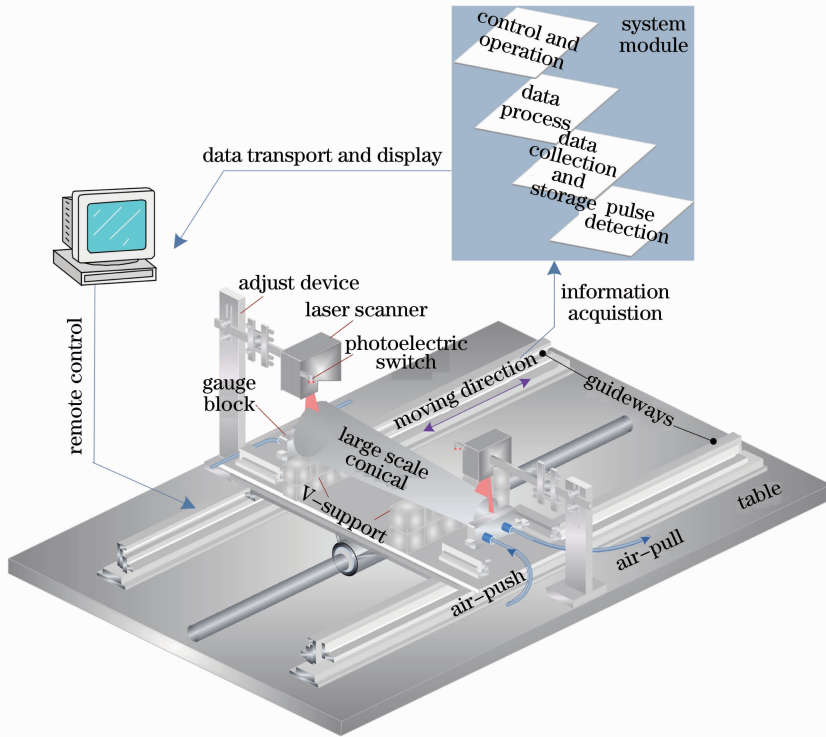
大尺寸圆锥体工件几何尺寸检测系统图
